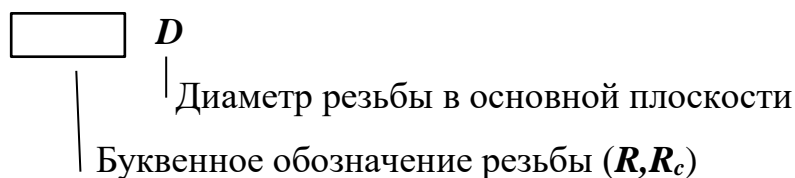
Образец обозначения трубной цилиндрической резьбы
